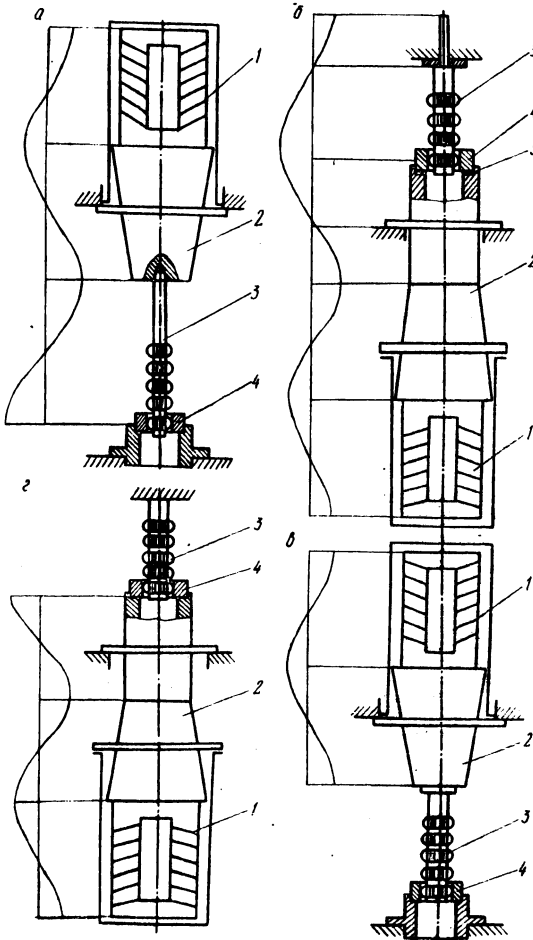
Схемы колебательных систем для калибровки шлицевых отверстий:
